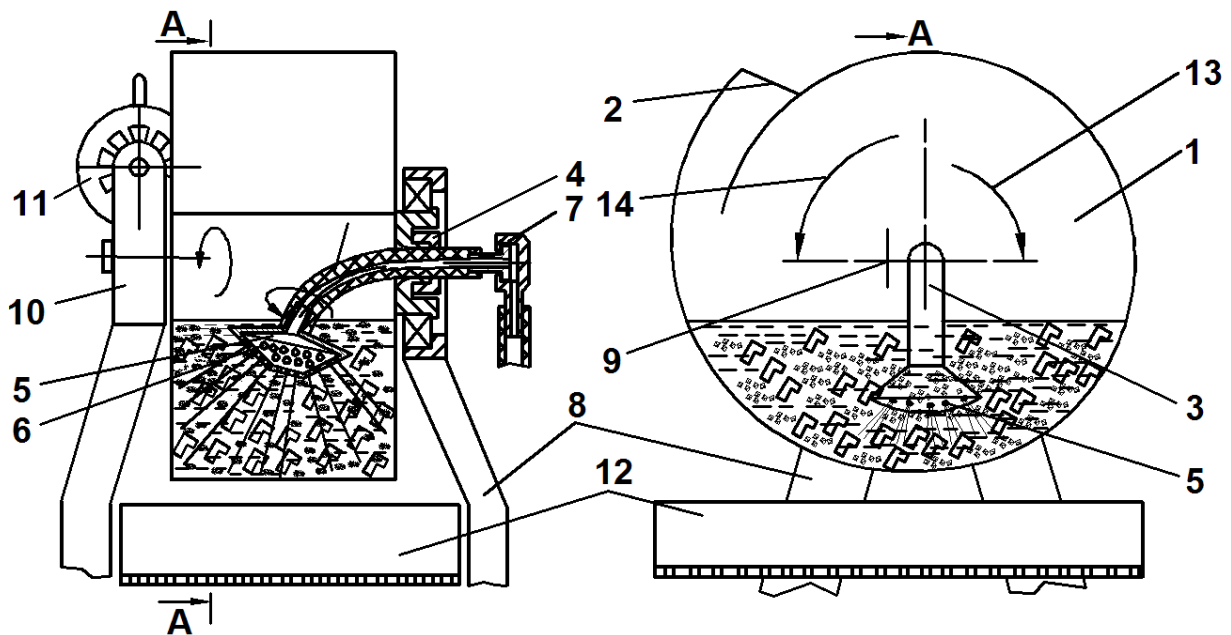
Принципова схема абразивної установки для обробки затопленими струменями зі спіралеподібною робочою камерою
